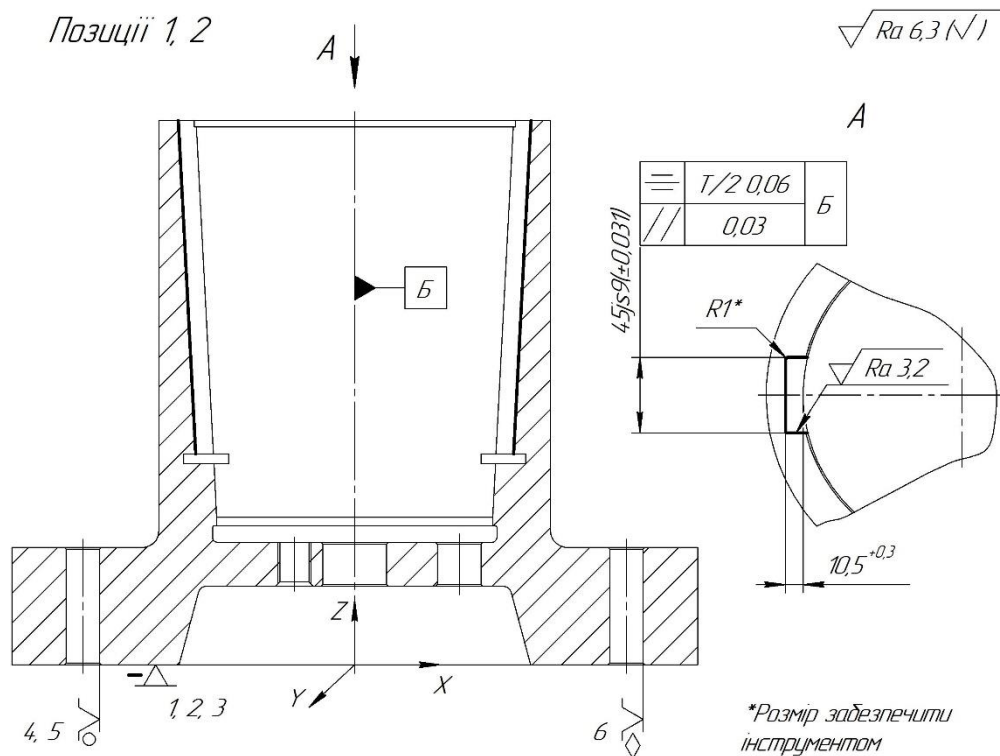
Схема базування заготовки на операції довбальній 120
